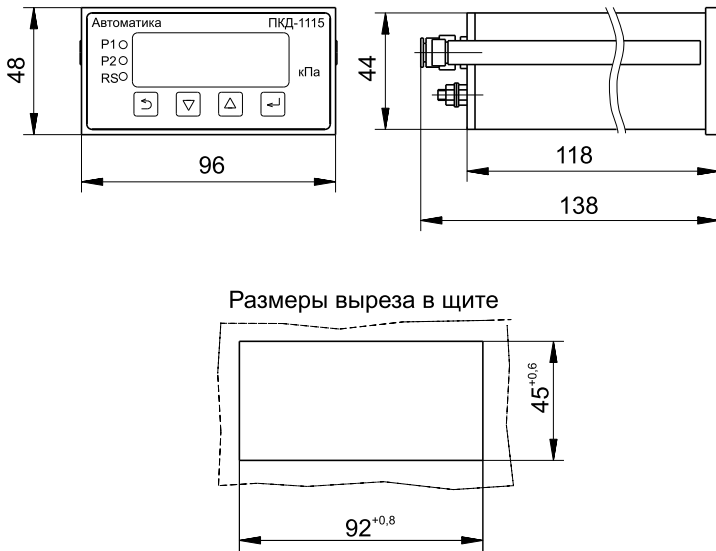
Корпус ПКД-1105, ПКД-1115 для щитового монтажа
